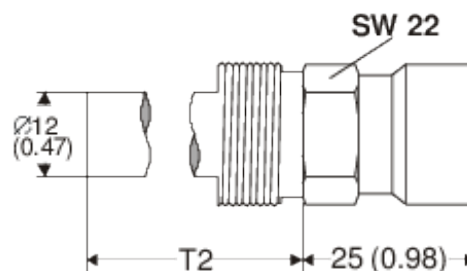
Vainas de inmersión, dimensiones en mm (inches)
